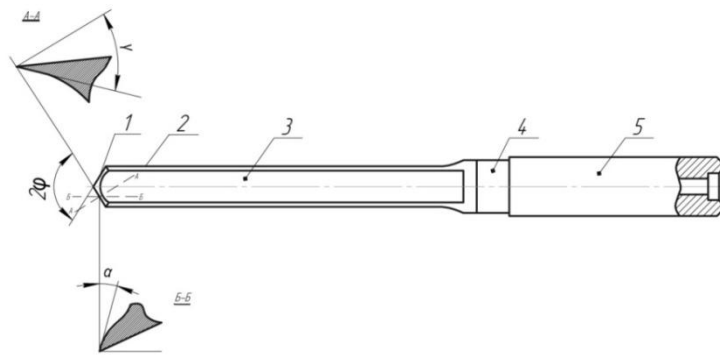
Схема реверсивного свердла для обробки ПКМ
